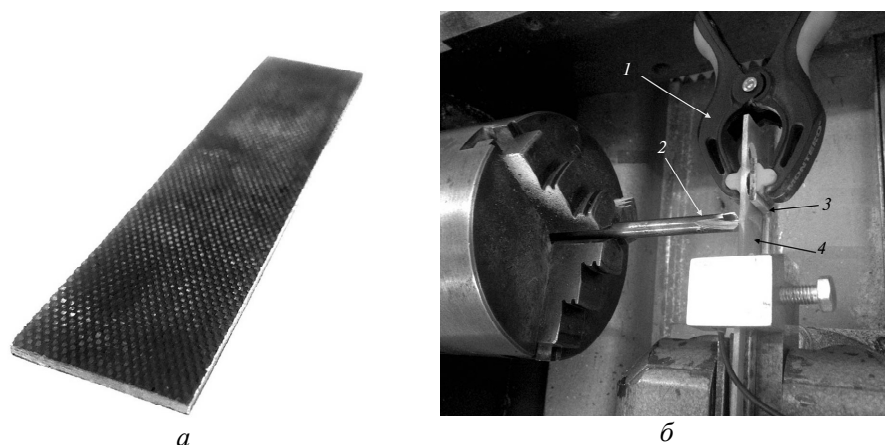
Сверление стеклопластика: заготовка из стеклопластика (а), установка заготовки на станке (б); 1 – крепежная струбцина; 2 – сверло; 3 – упорная пластина; 4 – заготовка.
